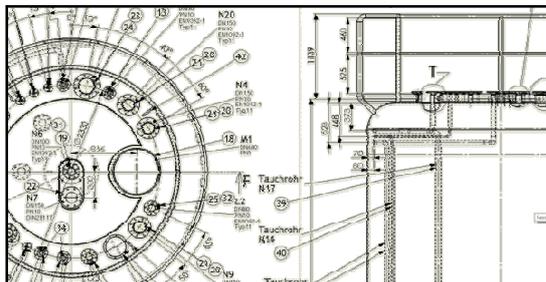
Ausführungs-Schweißzeichnung
